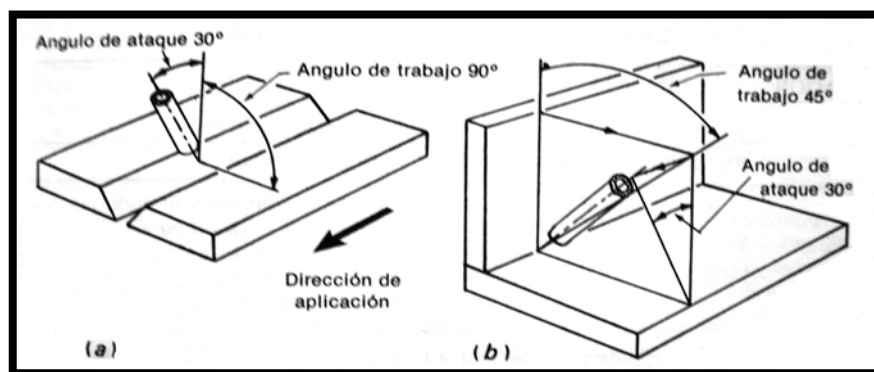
(a) Posición del electrodo en posición plana (b) Posición del electrodo en posición horizontal
